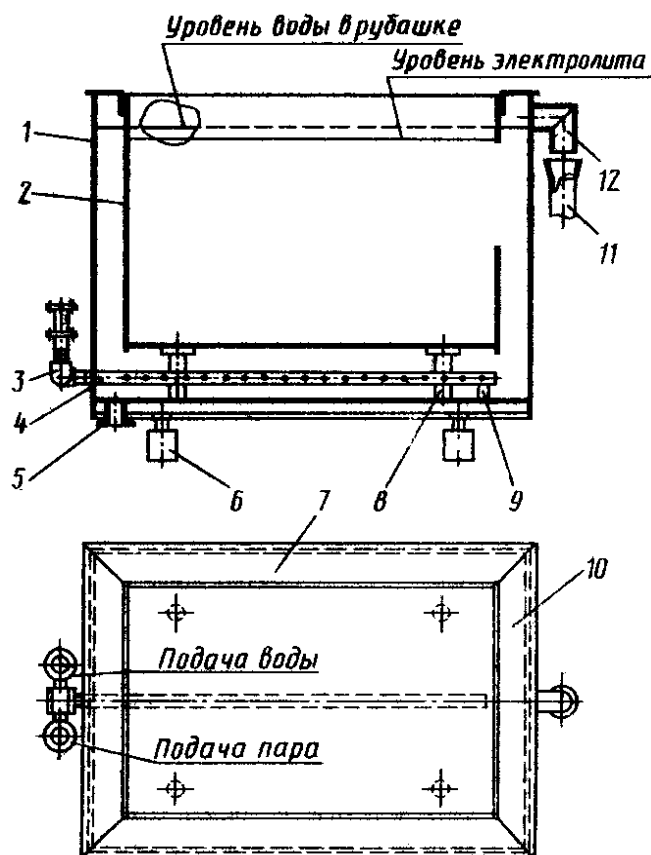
Ванна с пароводяной рубашкой: 1 — внешняя ванна; 2 — рабочая ванна; 3 — тройник; 4 - барботер; 5 — патрубок слива вода на рубашки; 6 — ножка ванны; 7, 10 — обвязка из уголков; 8 — ножка рабочей ванны; 9 — опора; 11 — воронка; 12 — патрубок.
